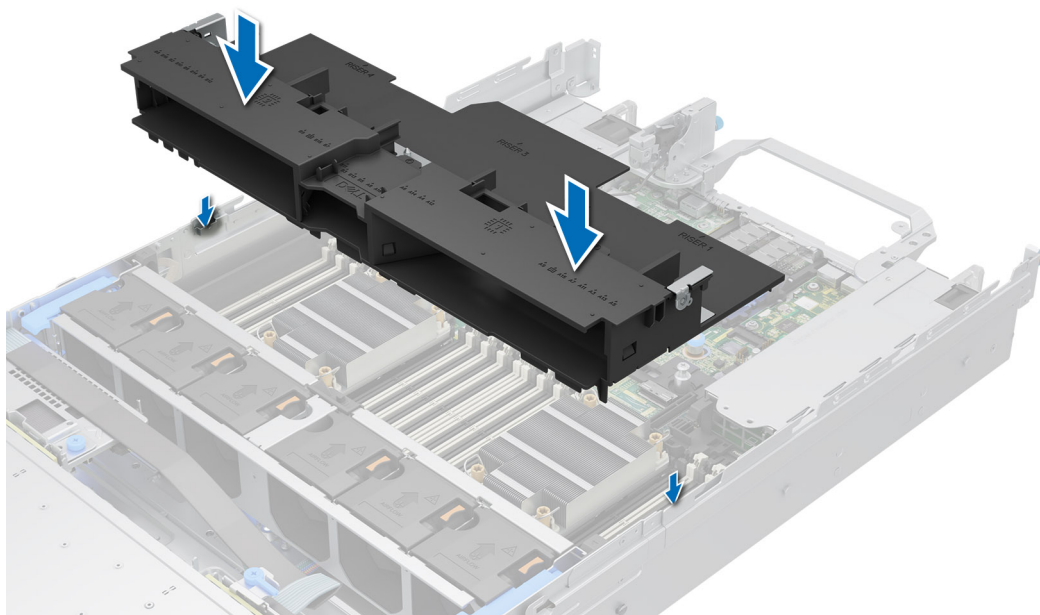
Anbringen des GPU-Kühlgehäuses
